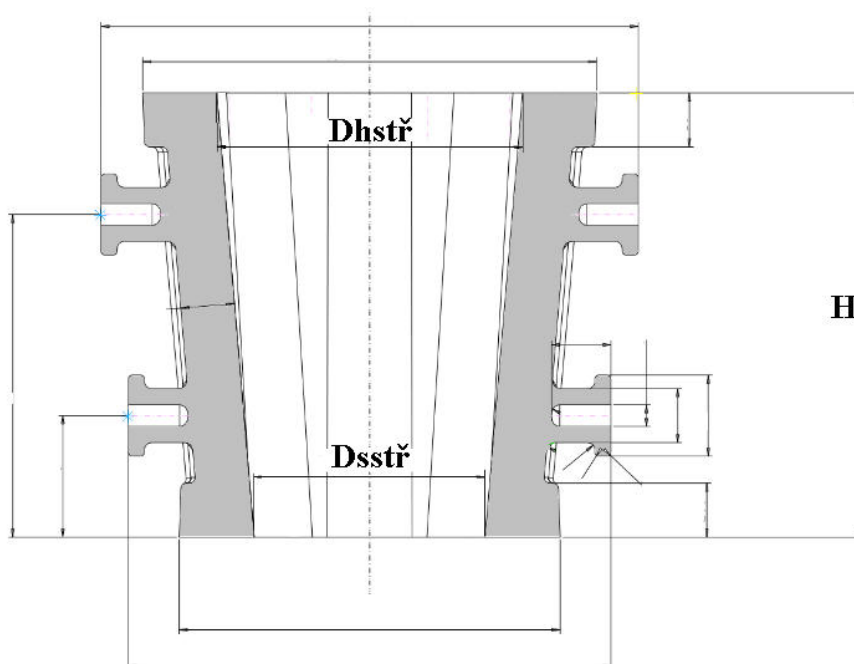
příčný řez upravenou kokilou – horní plocha
